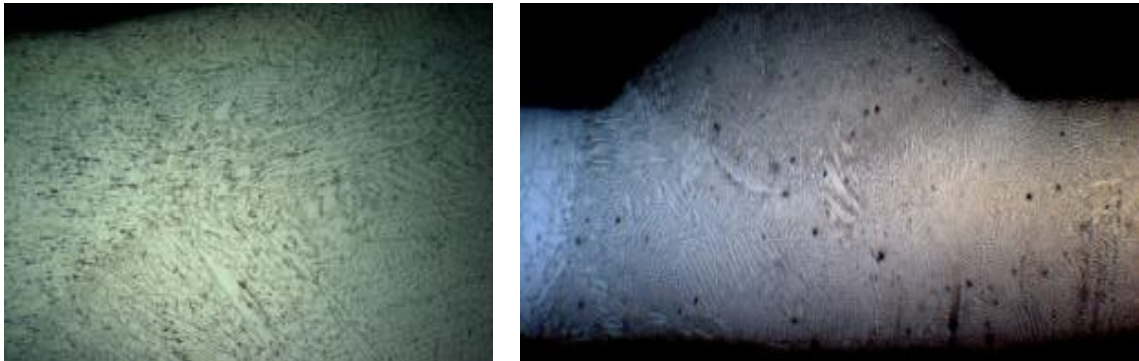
Exemples pris des éprouves de soudure de TIG à Haynes 230 :
